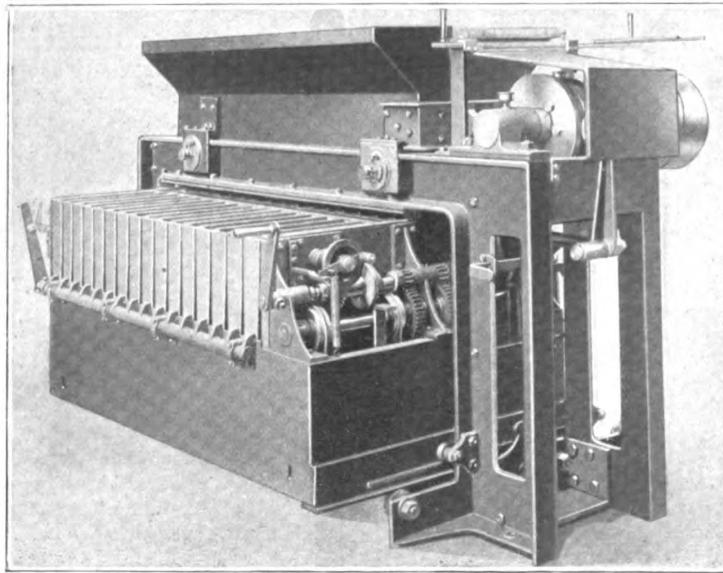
Holzdraht-Gleichlege- und Sammelmaschine.
